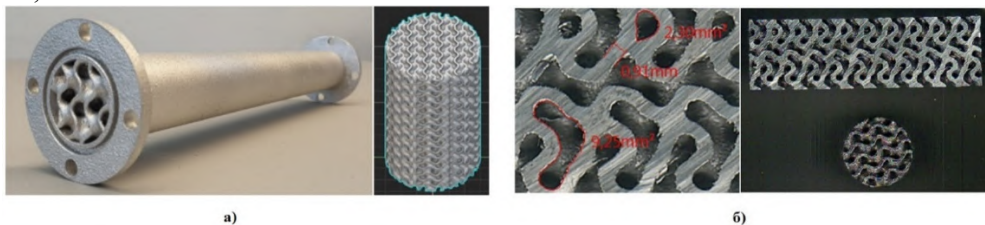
Насадочное устройство изготовленное на 3D принтере:
